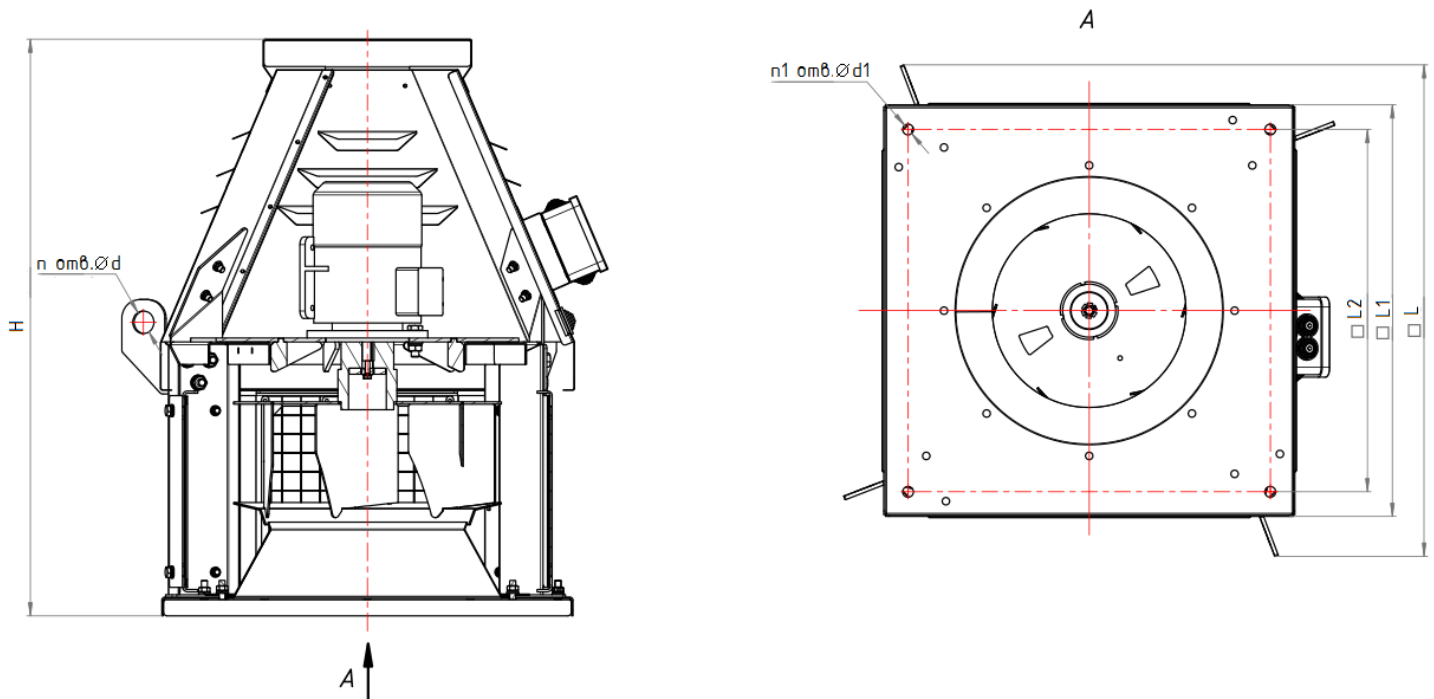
Габаритные, присоединительные размеры и общий вид вентиляторов ВКРС-РВ
